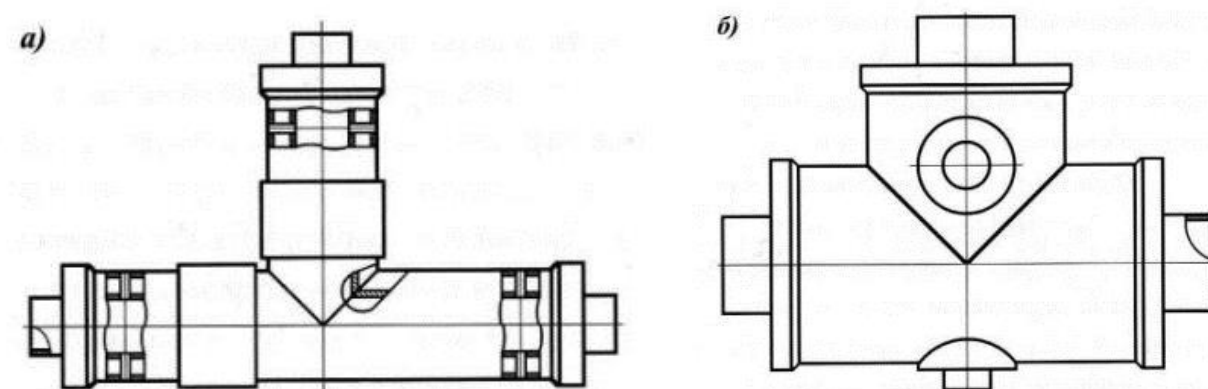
Конструктивные схемы тройников унифицированных колен (а – с дисковыми опорами; б – с цапфовыми опорами)
